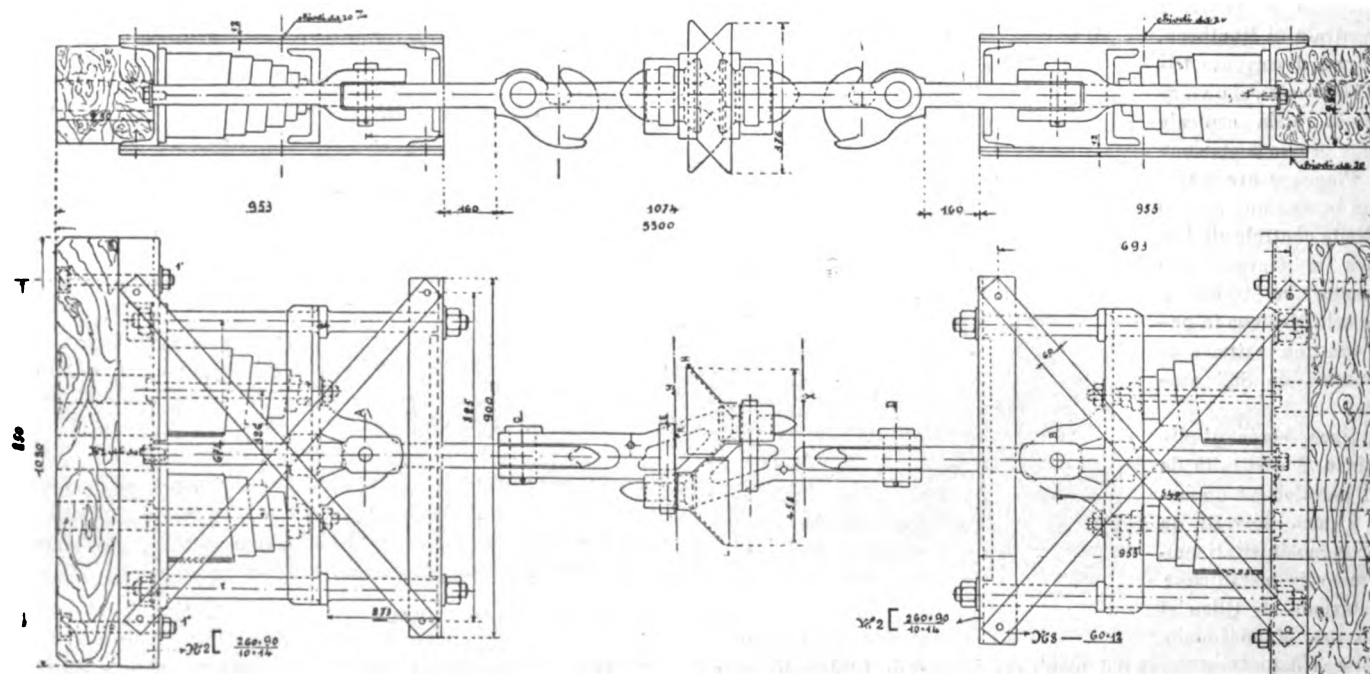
Apparecchio Breda. - Elevazione e pianta.
